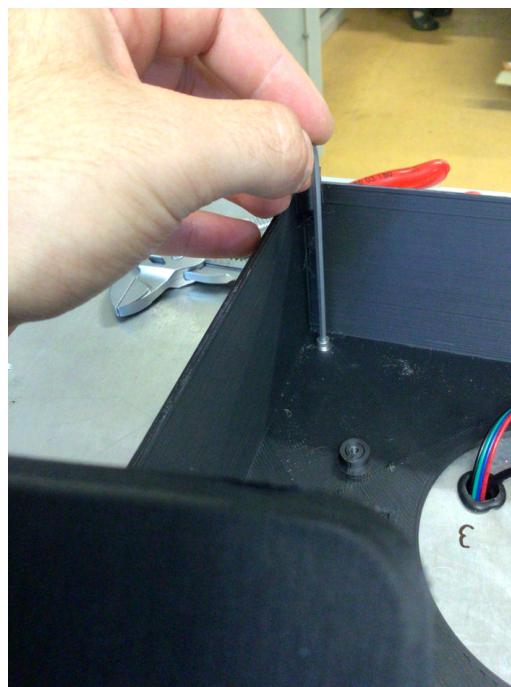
Gehäuseträger auf Alu-Platte verschrauben
